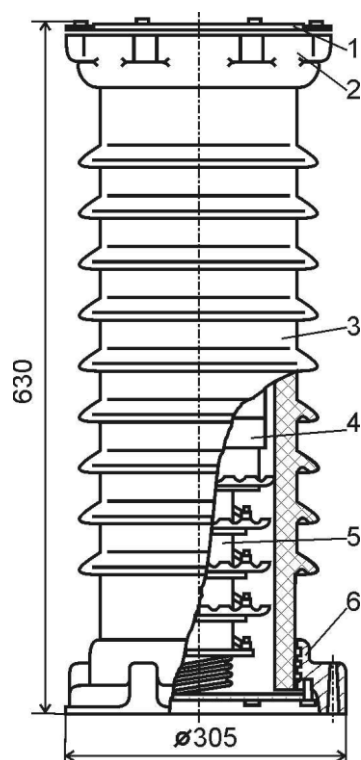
Облегченный вентильный разрядник на 10 кВ: 1 – верхняя кромка; 2 – верхний флянец; 3 – фарфоровый корпус; 4 – блок рабочих сопротивлений – вилитовых дисков; 5 – блок искровых промежутков; 6 – нижний флянец
